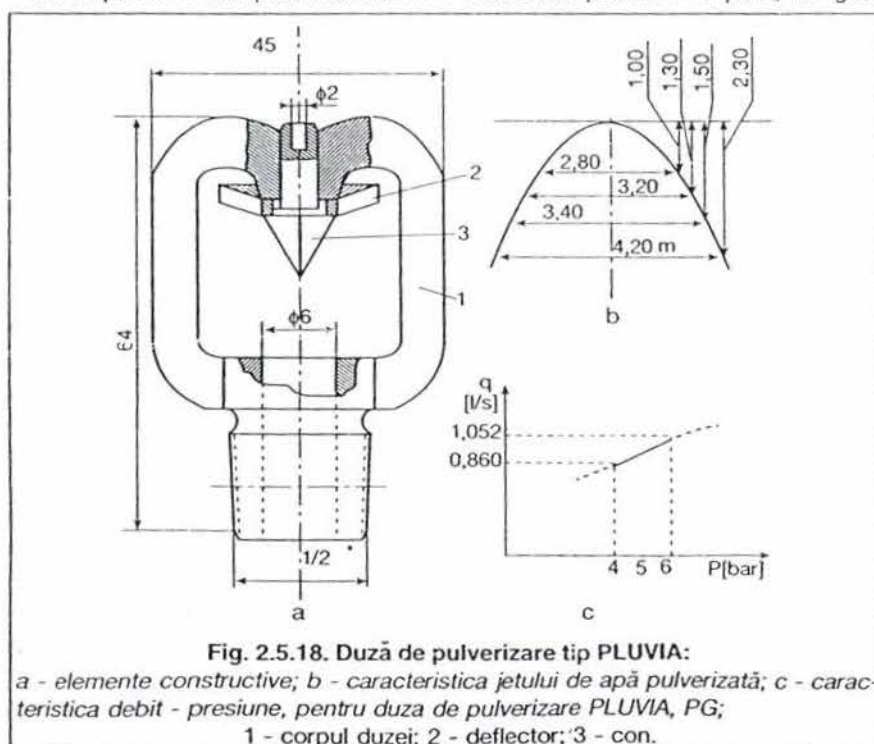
Duza de pulverizare tip PLUVIA:
